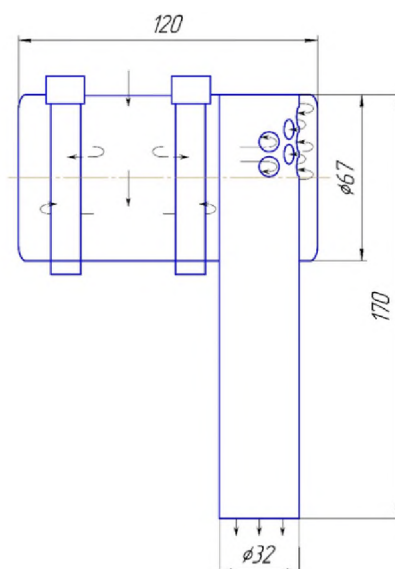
Конструктивная схема глушителя марки JMB SSA–ZDZ 80
